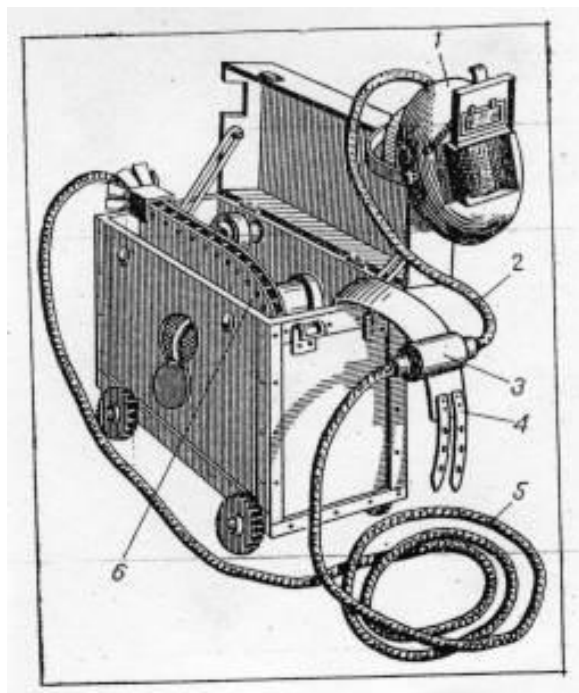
Щиток сварщика, оборудованный системой подачи очищенного воздуха от установки группового пользования: 1- щиток сварщика, оборудованный системой подачи чистого воздуха в зону дыхания сварщика; 2 – облегченный шланг; 3 – ремень поясной; 4- подогреватель воздуха; 5 – шланг; 6- вентилятор высокого давления типа ВПП - 4.
